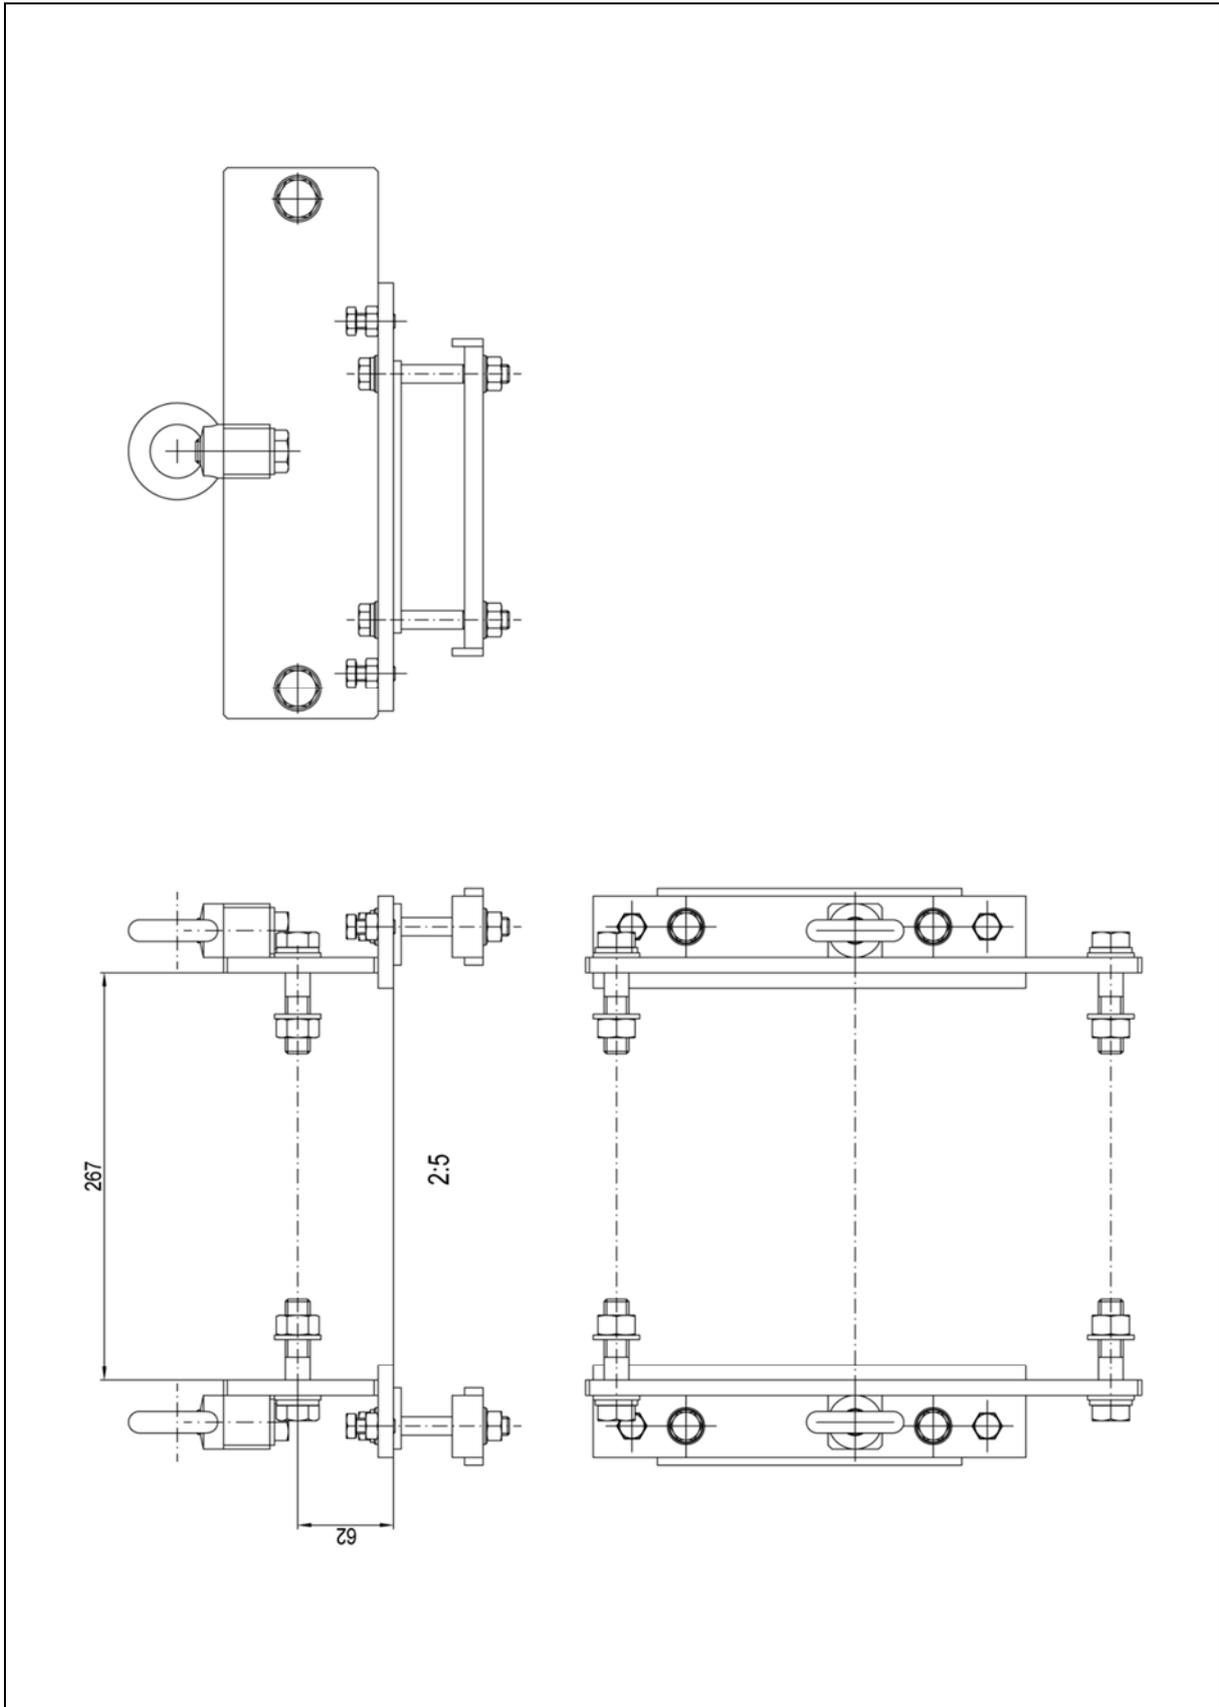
Halterungssatz für Typ 150 (Maße in mm)
